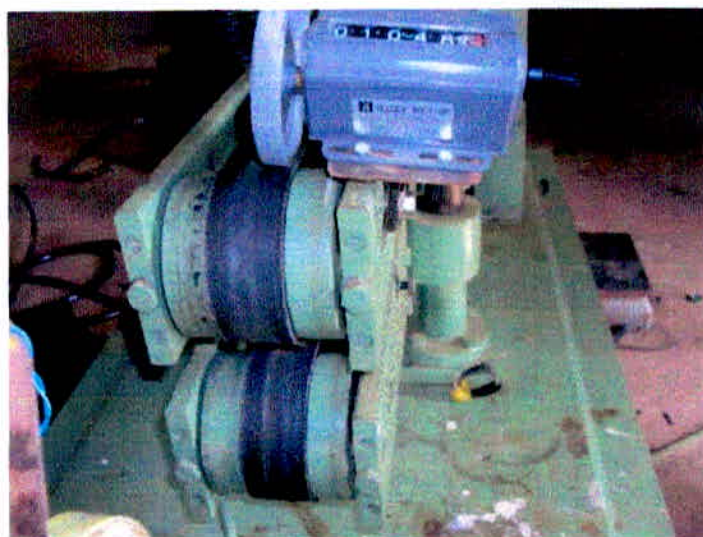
Entrada do Tubo nas lagartas Equipamento Reformado
